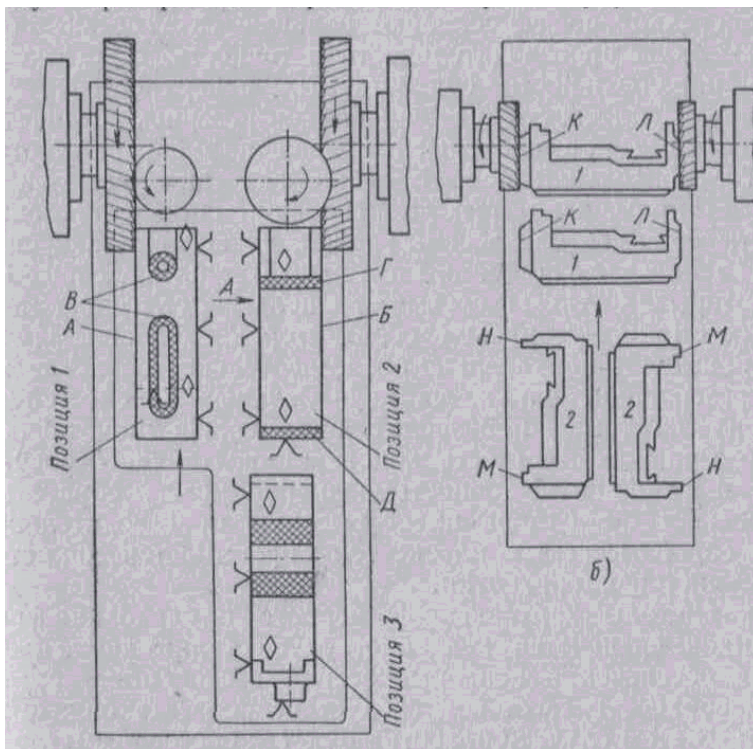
Обработка заготовок на продольно-фрезерных станках «в перекладку»: а – по однопоточной схеме; б – по двухпоточной схеме
